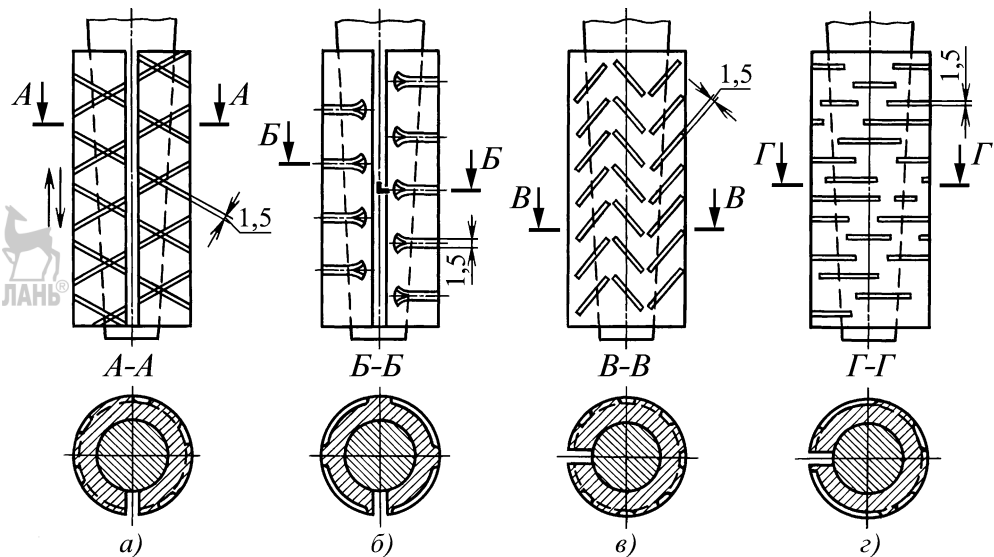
Притиры для доводки цилиндрических отверстий в виде стержней с канавками:
